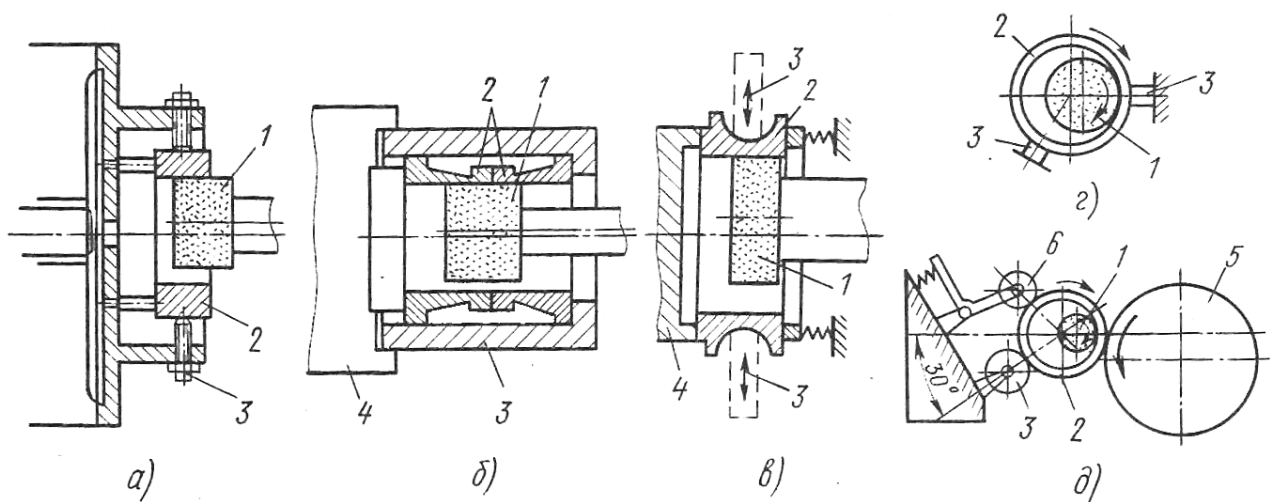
Схема базування деталей при внутрішньому шліфуванні [21]
